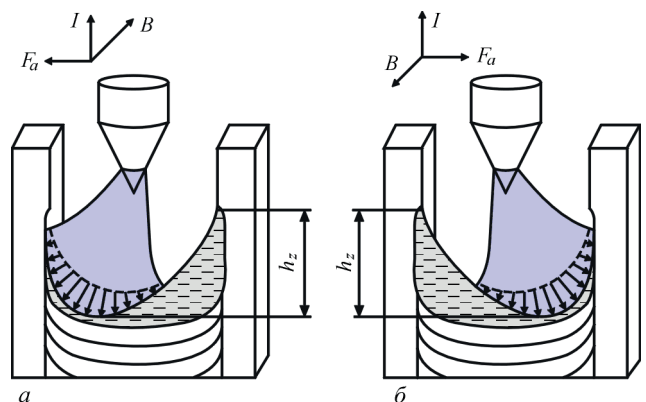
Схema оплавлення бокових стінок вузького зазору та розташування зварювальної дуги: а, б – крайні положення; h_z – висота шару металу шва, що наплавляється
